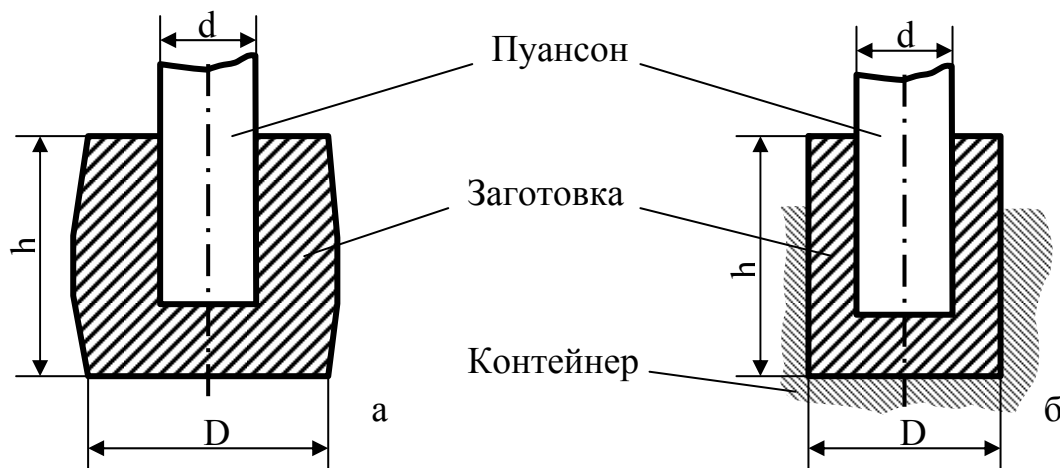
Прошивка заготовки: а – открытая; б – закрытая
